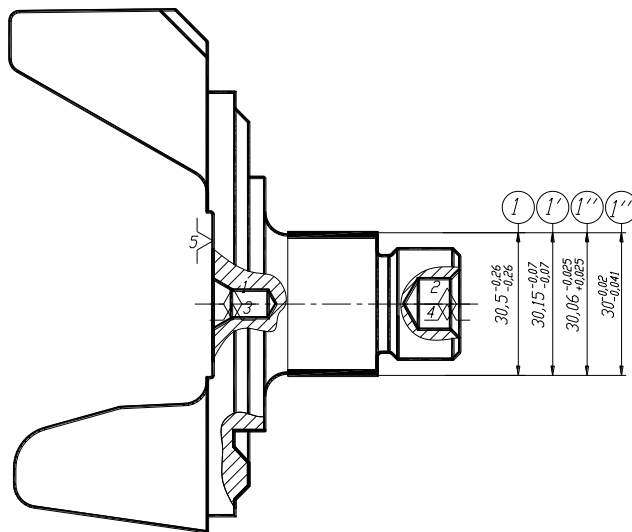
Обробка поверхні $\varnothing 30f7$
